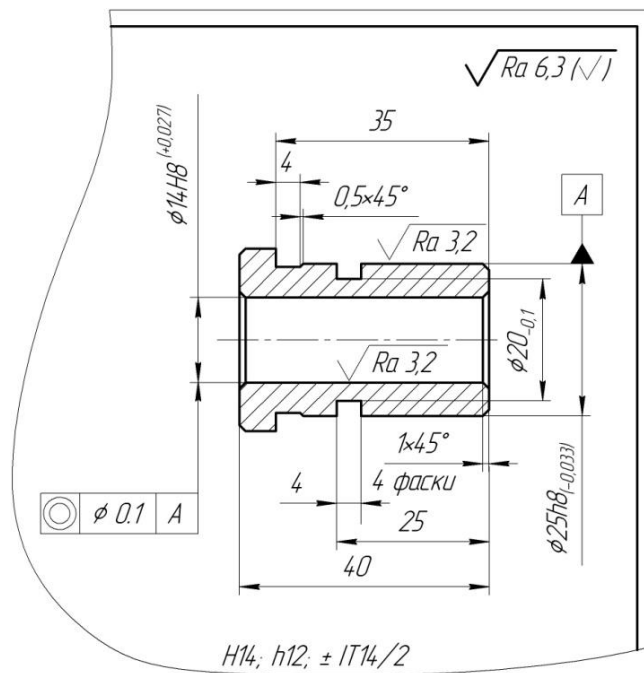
Фрагмент робочого креслення деталі типу «втулка»
